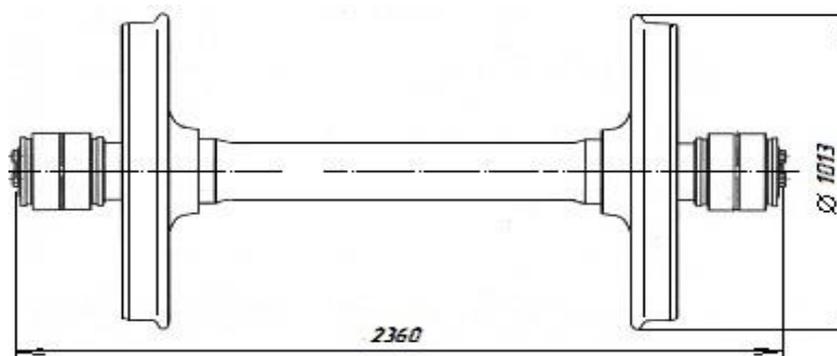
Колесные пары типа РУ1Ш-957-Г и РВ2Ш-957-Г с подшипниками под адаптер
